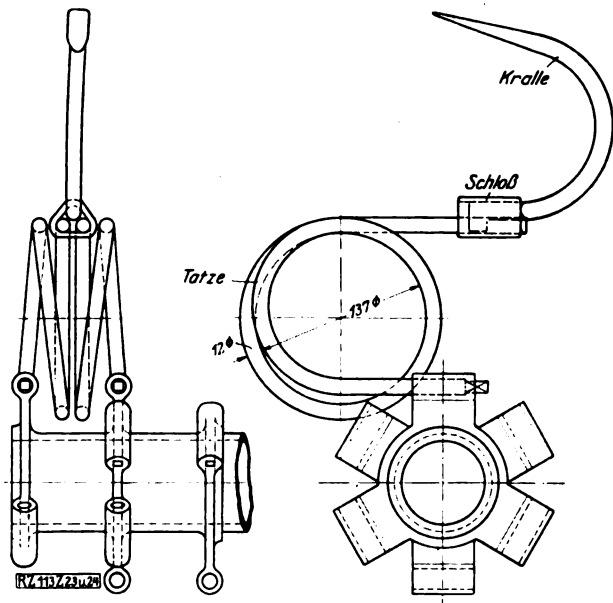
und 24. Befestigung des Arbeitswerkzeugs der SSW-Fräse.
